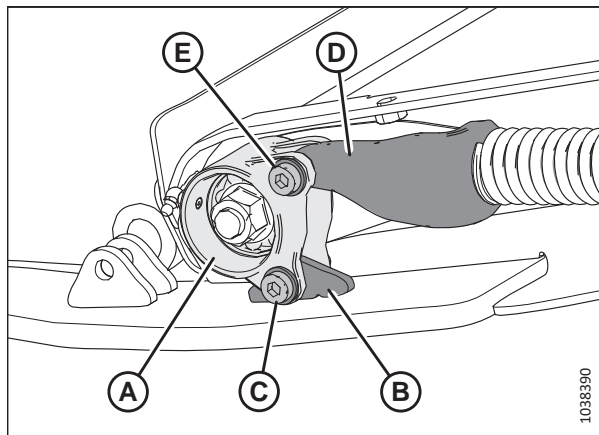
Rodamiento del rodillo tensor izquierdo
